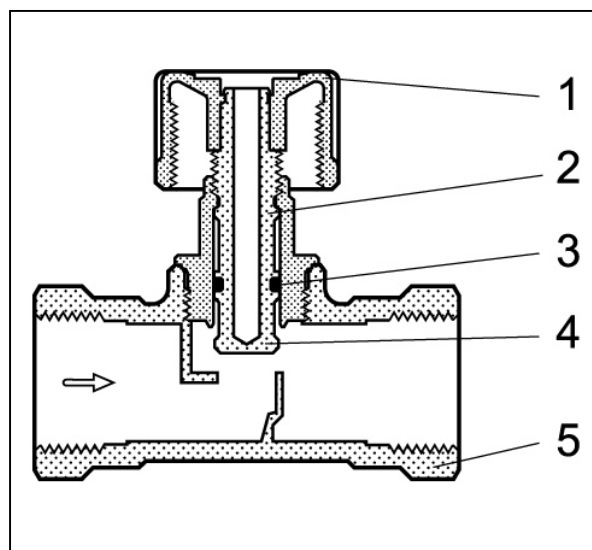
Ручной балансировочный клапан типа MSV-M.
